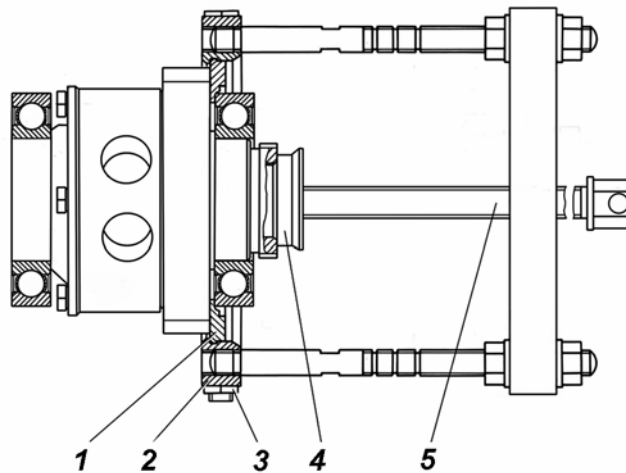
Снятие подшипника с шестерни дифференциала: 1 – вкладыш; 2 – опора; 3 – гайка; 4 – подпятник; 5 – винт
